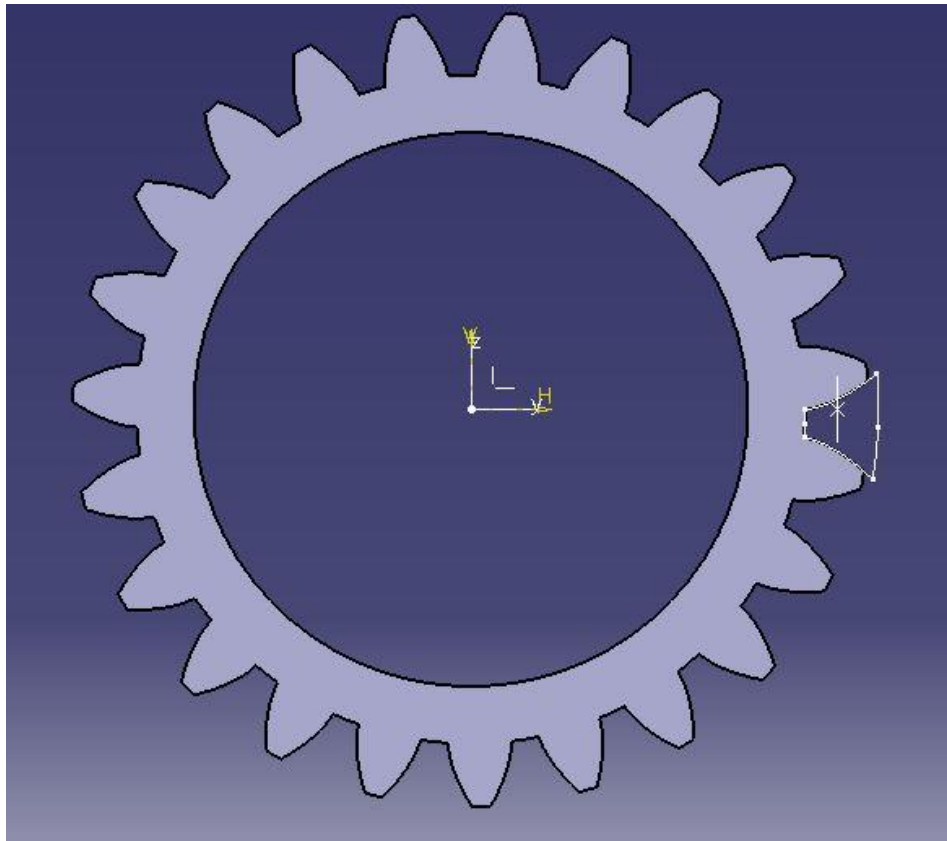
Diseño Engranaje 01. [Elaboración propia]
